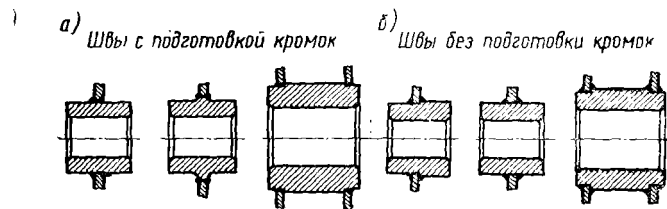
Сварные соединения дисков со ступицами:
